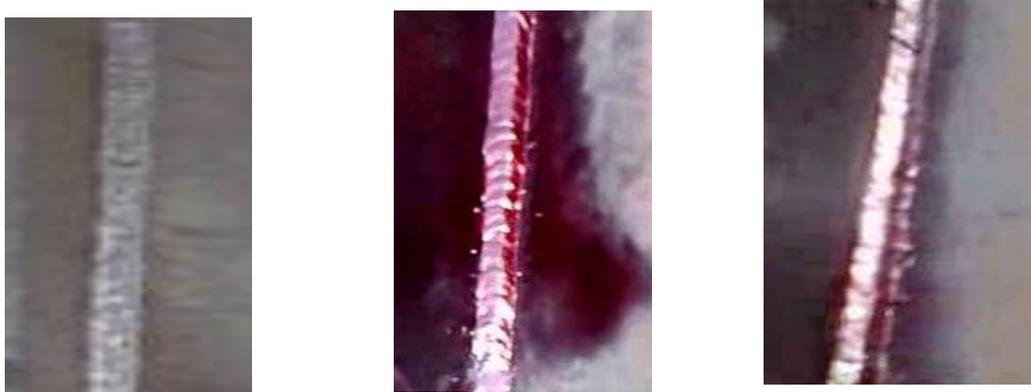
(a) Soldadura de filete (b) Aplicación del Penetrante (c) Aplicación del revelador (elaborado por el investigador).
